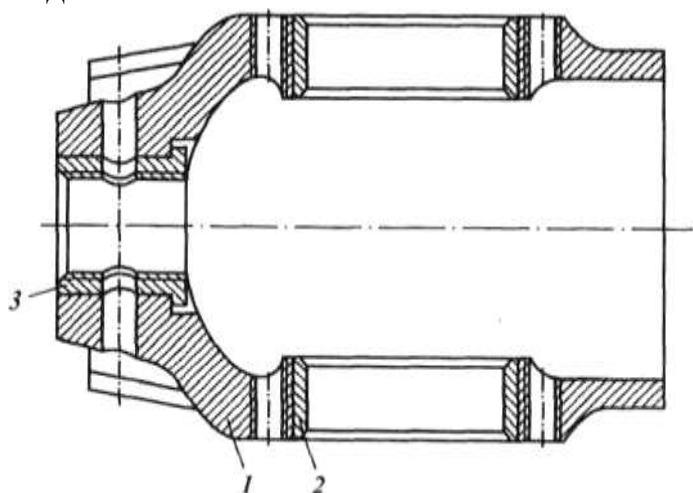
Корпус крейцкопфа, відремонтований з використанням додаткових ремонтних деталей: 1 - корпус крейцкопфа; 2 - ремонтна втулка під палець; 3 - ремонтна втулка під надставку штока
